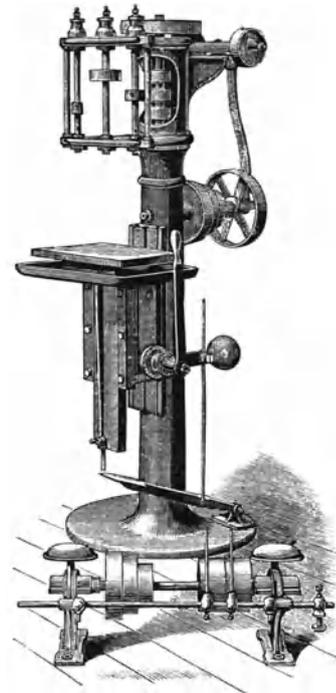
Gefühlsbohrmaschine der Pratt & Whitney Co. Hartford. 1876. Schnelllaufende, 3- und 4-spindlige Bohrmaschine mit Handvorhub durch Anheben des ausgewichteten Tisches mit Hand- oder Fußhebel. Größter Bohrdurchmesser des kleineren Modells 2 1/16". des größeren 1 1/2".
